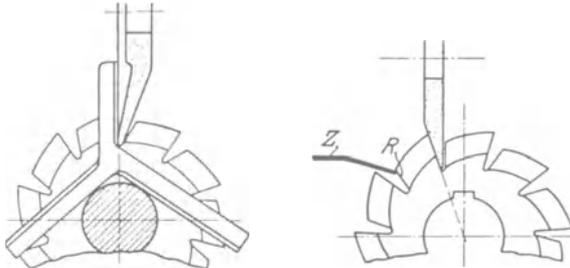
u. 353. Schärfen eines hinterdrehten Fräasers.
